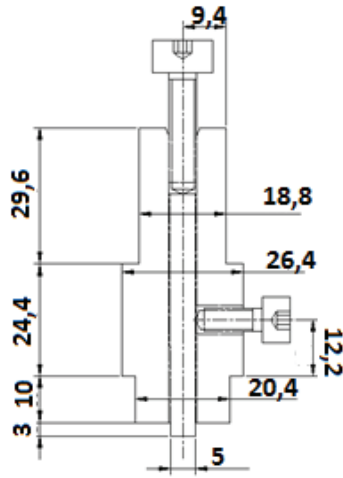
Birleştirme yöntemi ve birleştirme sırasında deney numunelerini tutan kalıp (Friction stir spot welding method and the sample assembly mould)
